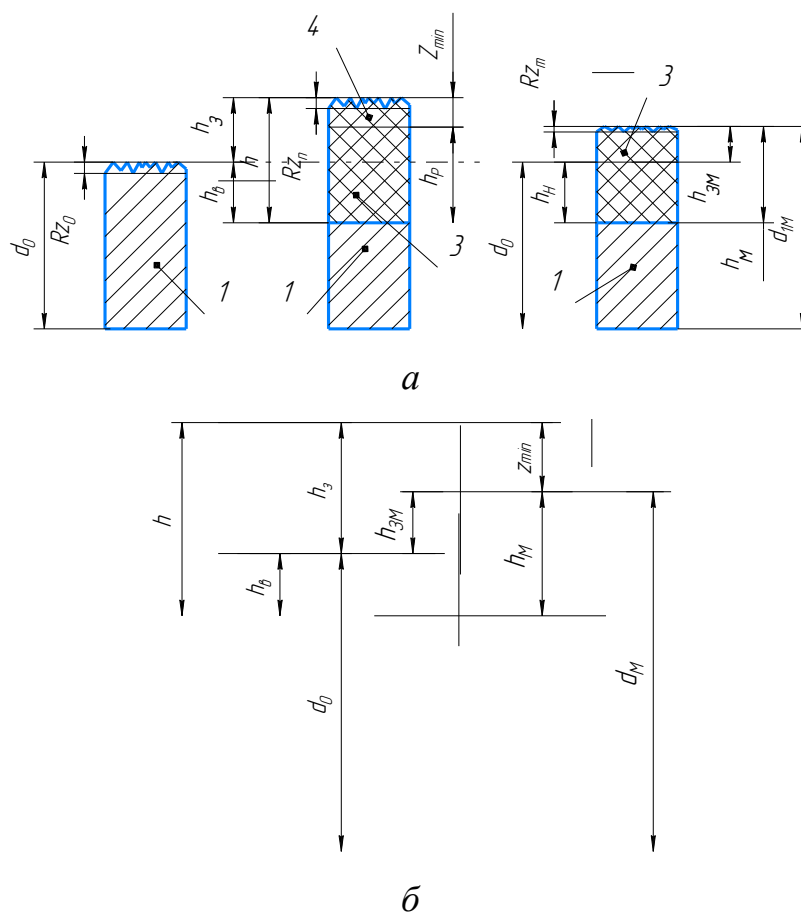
Схема утворення розмірів деталі після проведення мікродугового оксидування алюмінієвої заготовки для формування товстого робочого оксидного шару (а) та розмірний ланцюг (б) для випадку застосування механічної обробки
